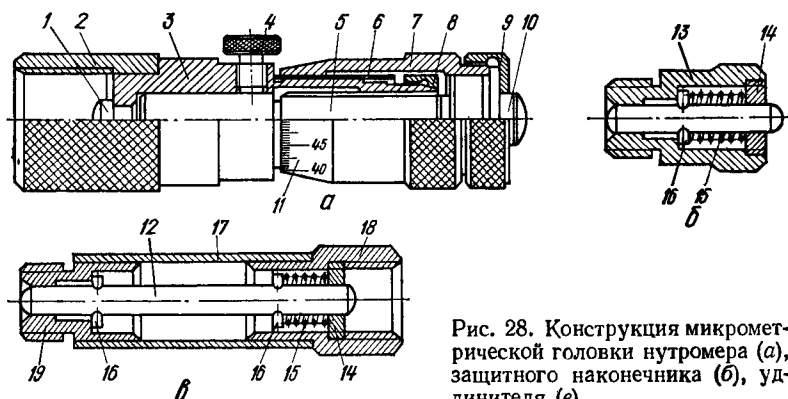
Конструкция микрометрической головки нутромера (а), защитного наконечника (б), удлинителя (в).
